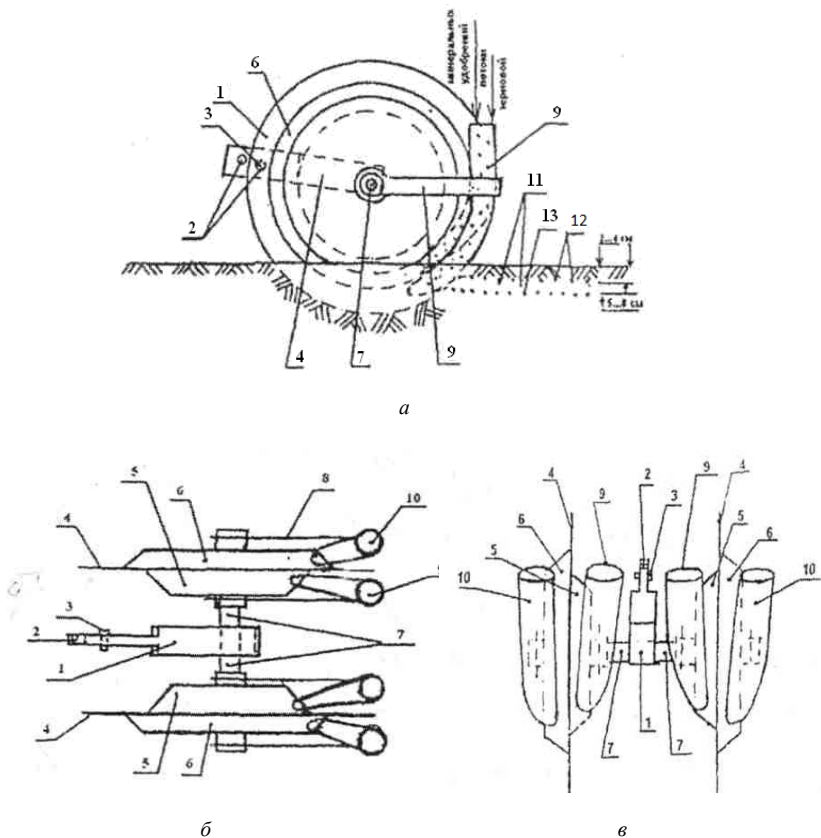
Комбинированный сошник с разновеликими ребрами и нулевым углом атаки дисков: *а* – вид сбоку; *б* – вид сверху; *в* – вид сзади; 1 – корпус; 2 – отверстия; 3 – болт; 4 – диски; 5, 6 – ребры-бороздкообразователи-уплотнители; 7 – ось; 8 – пластина; 9, 10 – семянаправители; 11 – бороздки; 13 – гранулы минеральных удобрений; 12 – семена
